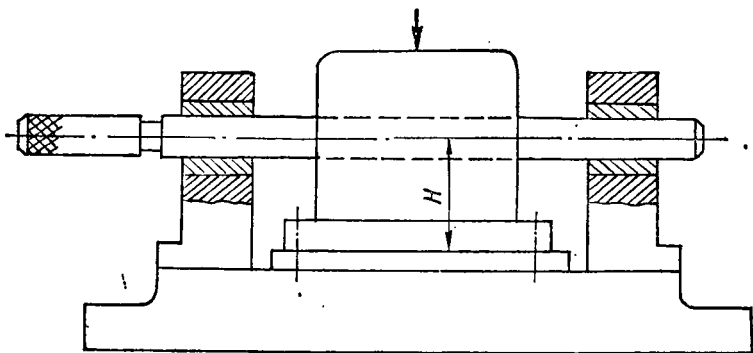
Схема проверки расточного приспособления по эталонной детали
